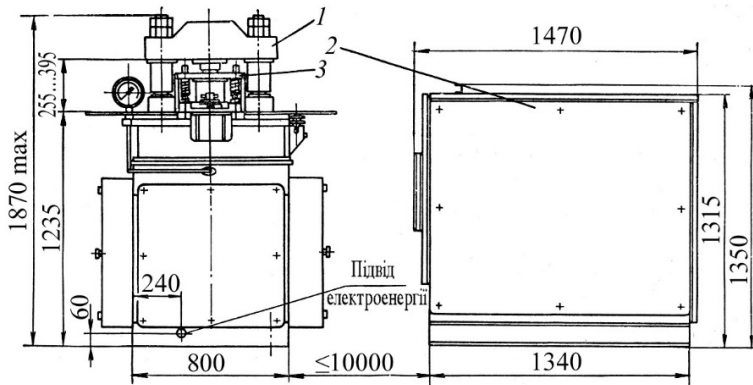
Схема машини К-609М для зварювання корпусів силових напівпровідникових приладів:
